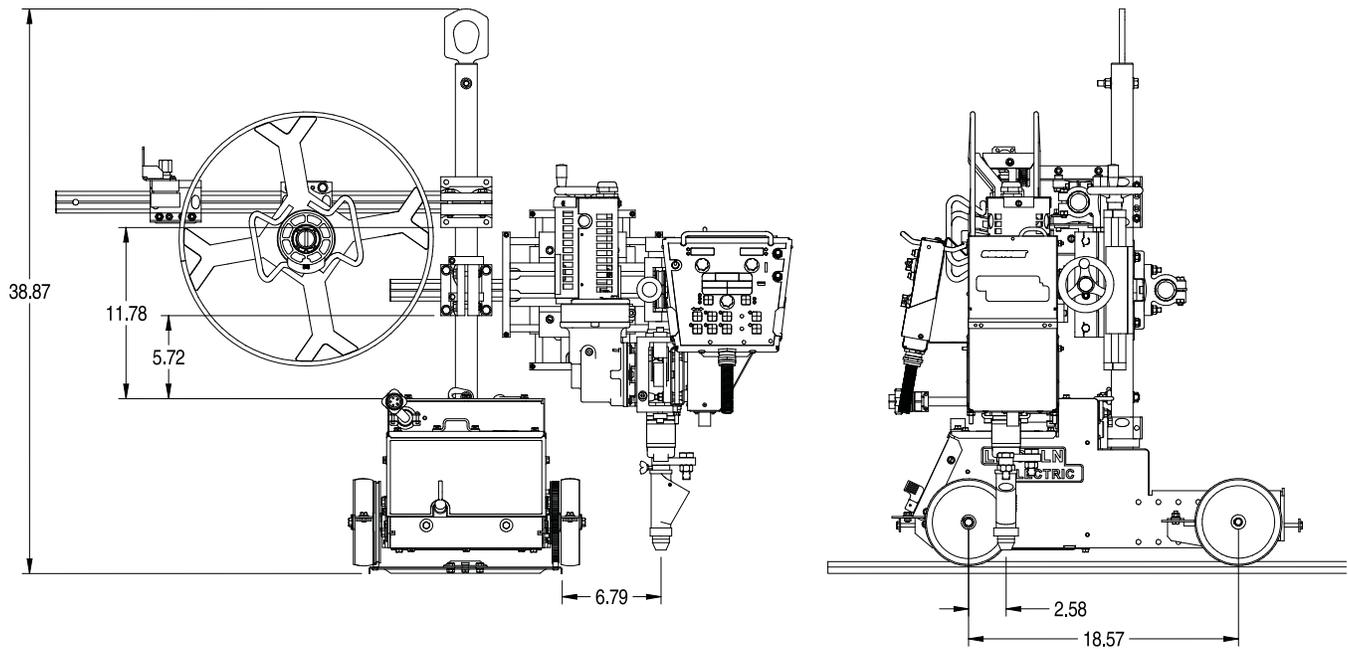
JUNTA A TOPE, VISTA FRONTAL DE LA RUEDA GUÍA, 3 RUEDAS
